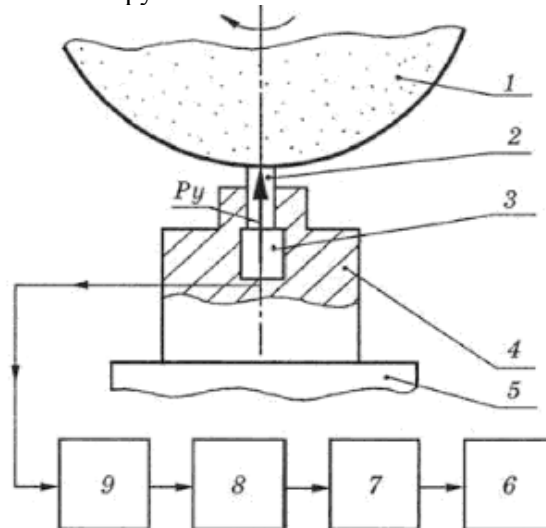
Схема пристрою для акустичної емісійної діагностики: 1 - шліфувальний круг; 2 - оброблюваний зразок; 3 - п'єзоелектричний датчик; 4 - державка; 5 - стіл верстата; 6 - принтер; 7 - комп'ютер; 8 - електронний блок; 9 - попередній підсилювач
